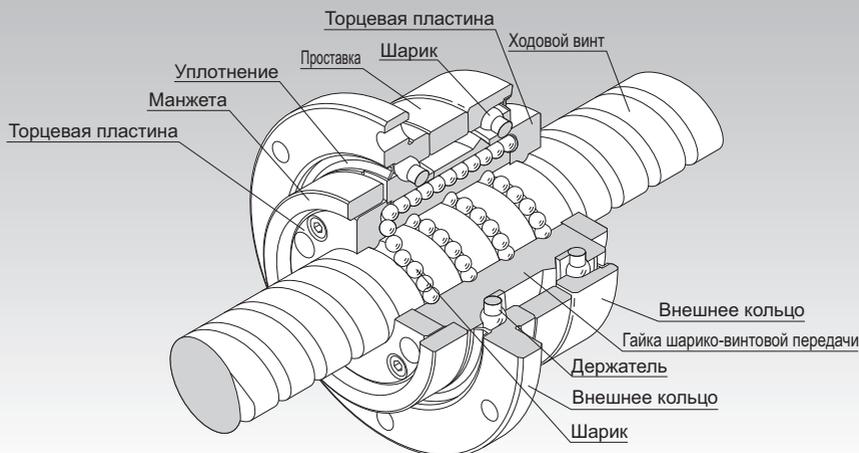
Конструкция шарико-винтовой передачи с поворотной гайкой и большим шагом резьбы модели BLR
